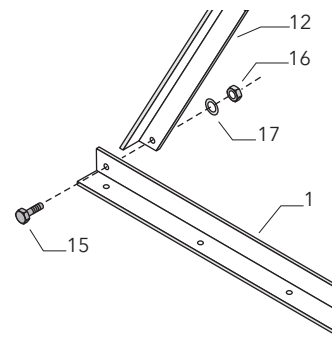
Kollektorprofil mit Bodenprofil verschrauben.
